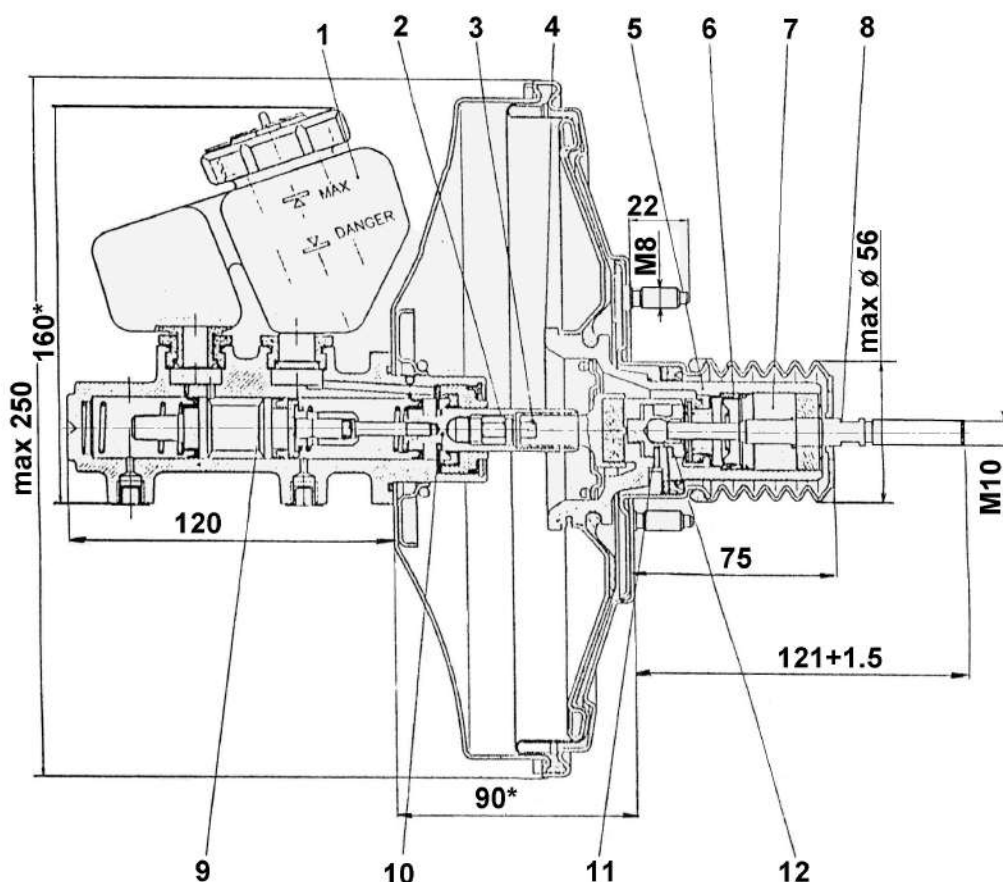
Схема вакуумного усилителя в сборе с главным тормозным цилиндром: 1- бачок; 2- упорный наконечник штока; 3- шток; 4- диафрагма; 5- корпус клапанов; 6- уплотнитель клапанов; 7- воздушный фильтр; 8- толкатель; 9, 10- поршни главного тормозного цилиндра; 11- канал; 12- поршень вакуумного усилителя
